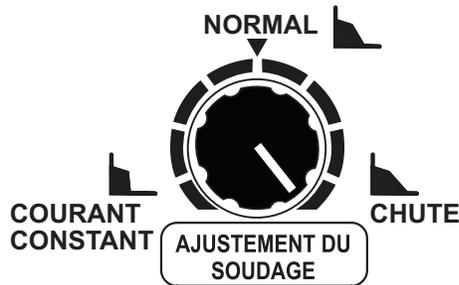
Bouton de réglage du soudage (Chute)
